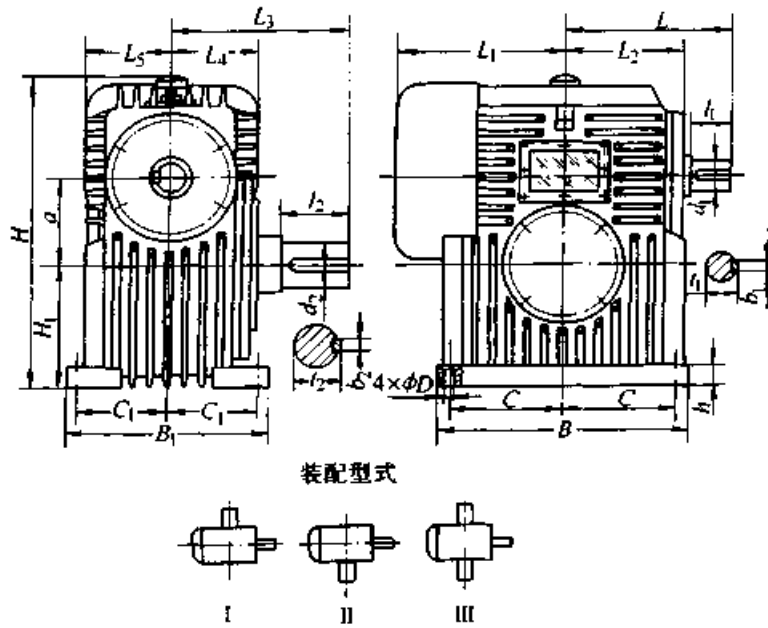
PWO 型减速器外形尺寸及装配型式 (整体式)
